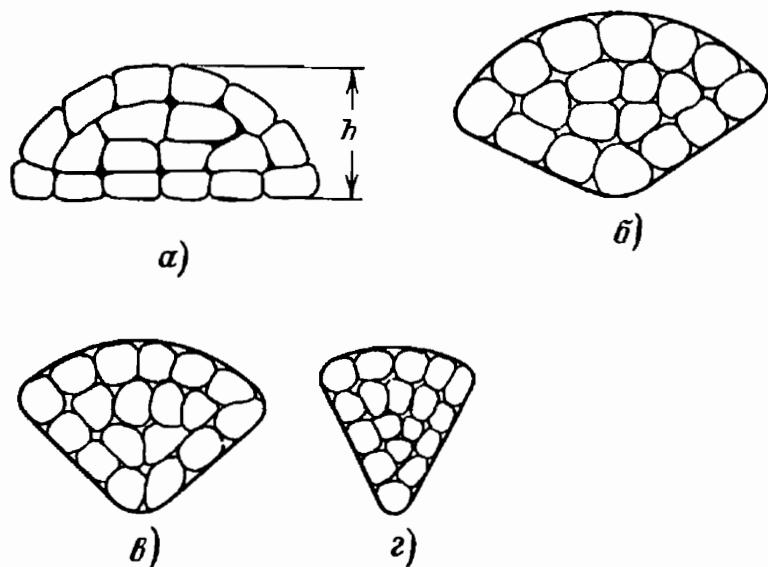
Схема уплотненных токопроводящих жил силовых кабелей.
